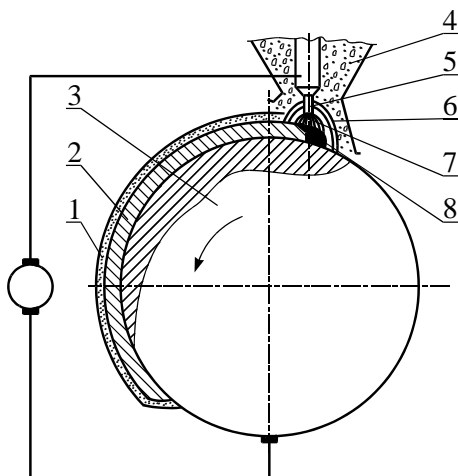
Схема наплавлення деталей під шаром флюсу:
